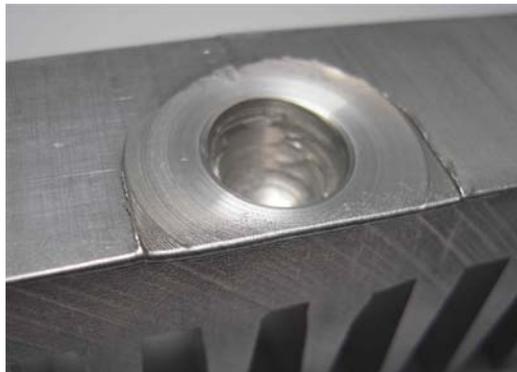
Das Werkzeug wird aus dem Füge­spalt herausgezogen. Die Schweißnaht ist sofort belastbar nachdem das Werkzeug abgehoben hat. Durch die Verbindung der Bauteile unterhalb der Schmelztemperatur ist der Verzug sehr gering.
